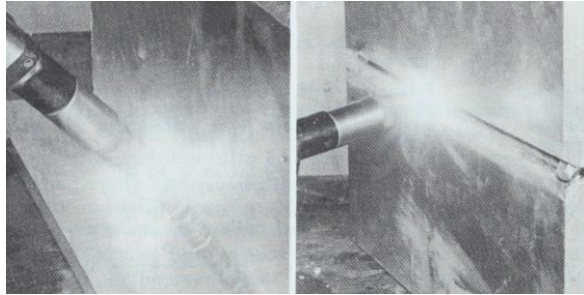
横位置的角接接头和对接接头的 MIG 焊接
